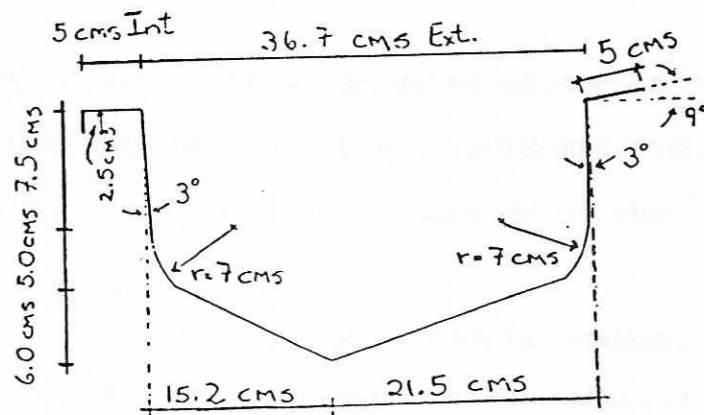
Contrapropuesta de canaleta; dimensiones y diseño para moldear por termoformado
